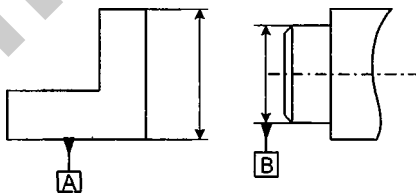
Правила нанесения на чертежах деталей условных обозначений баз
